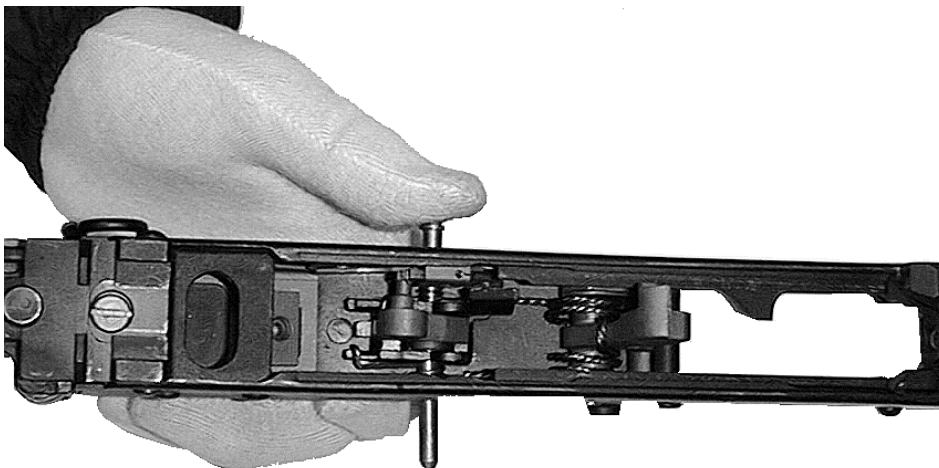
Przyłączanie mechanizmu przerywacza serii
